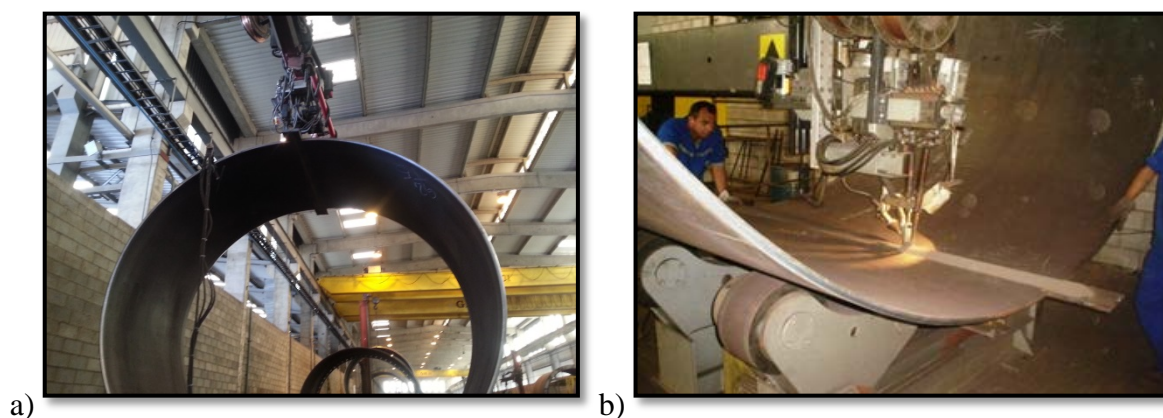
Soldadura longitudinal a) Exterior; b) Interior.
